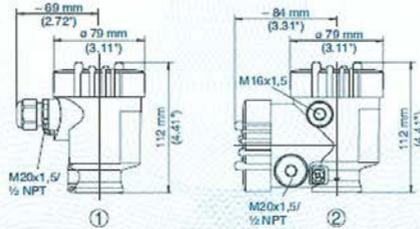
Пластиковий корпус (1 – однокамерний; 2 - двохкамерний)
